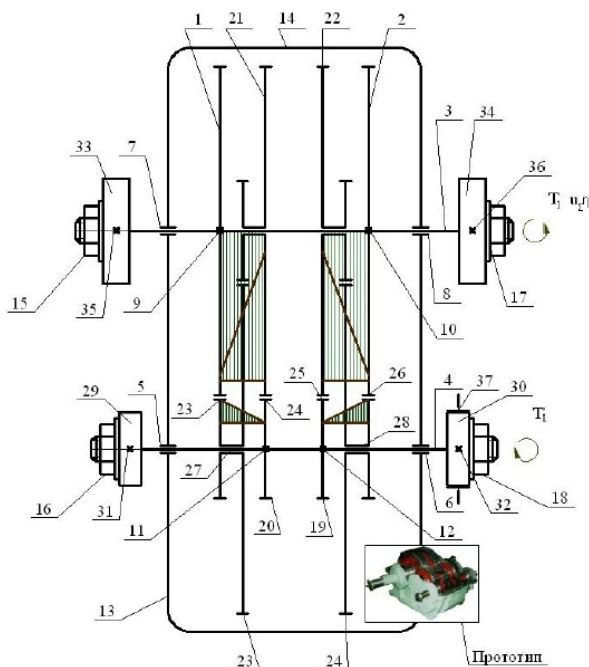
Кинематическая схема цилиндрического двухпоточного трехступенчатого пакетного редуктора
